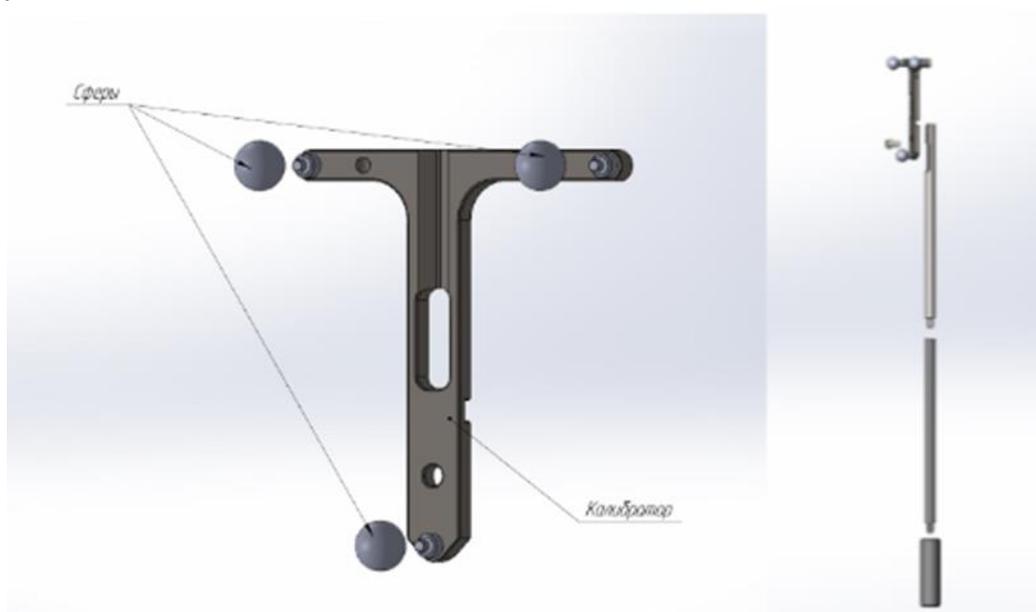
Схема сборки калибратора с тремя отражающими сферами (справа – установка калибратора на мачту)
